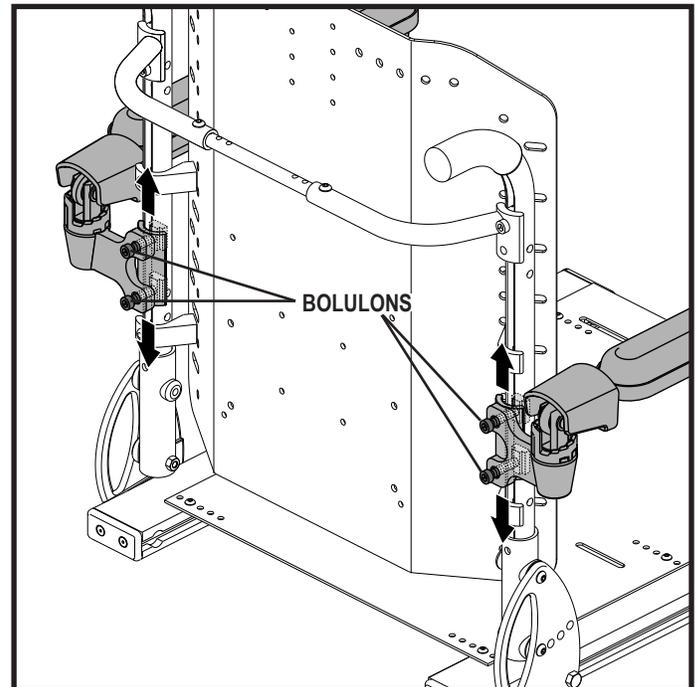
Réglage en hauteur des accoudoirs Cantilever non fixée sur la barre
